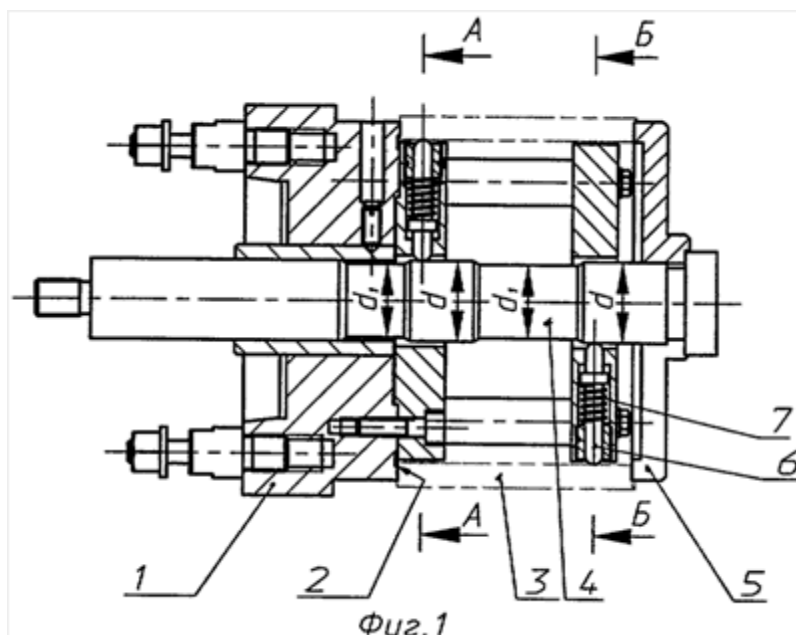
Устройство патенту РФ 2320458, продольный разрез
